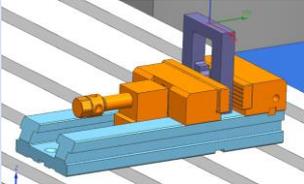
Situación de las piezas abrazadera en el conjunto de la estructura.
